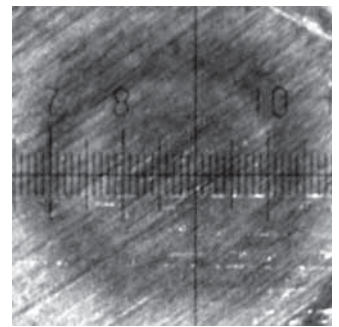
Внешний вид поверхности ЗЛВ на стали P18
